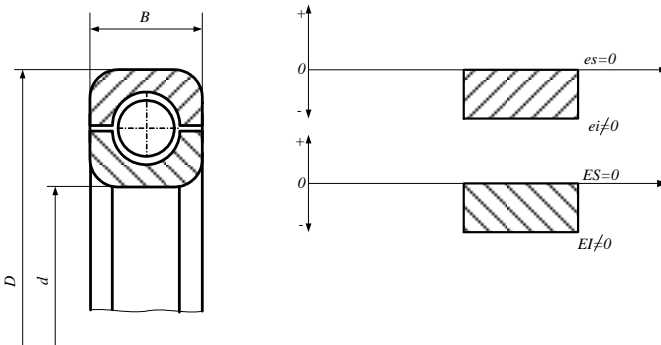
Розташування полів допусків на діаметри кілець кулькових підшипників
